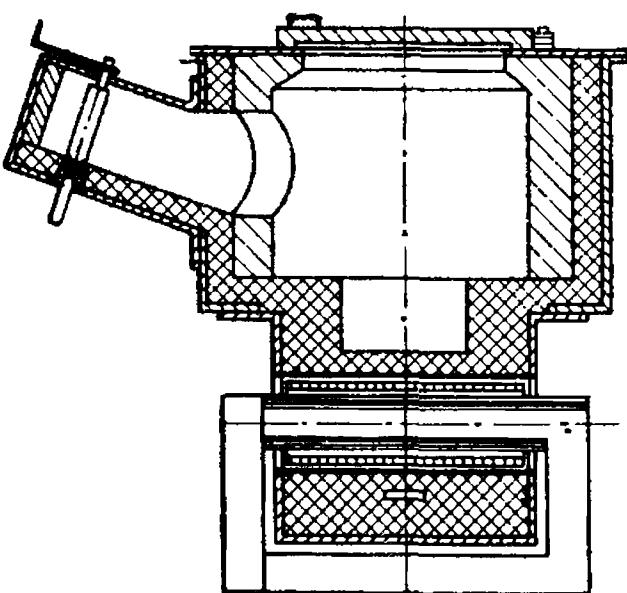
Плавильно-раздаточная печь для плавки и полунепрерывной разливки меди и ее сплавов
